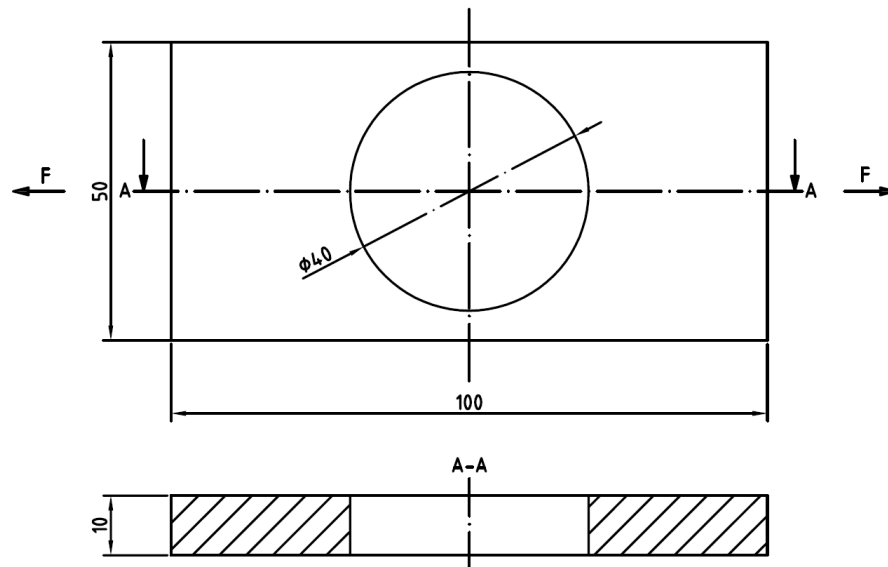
Geometria e direção de carregamento do provete de placa com furo. Dimensões em mm.
